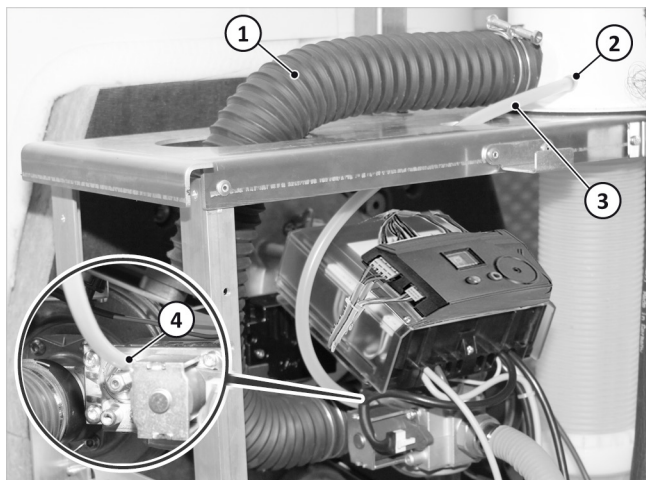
Zuluft- und Druckausgleichs-Schlauch aufstecken
